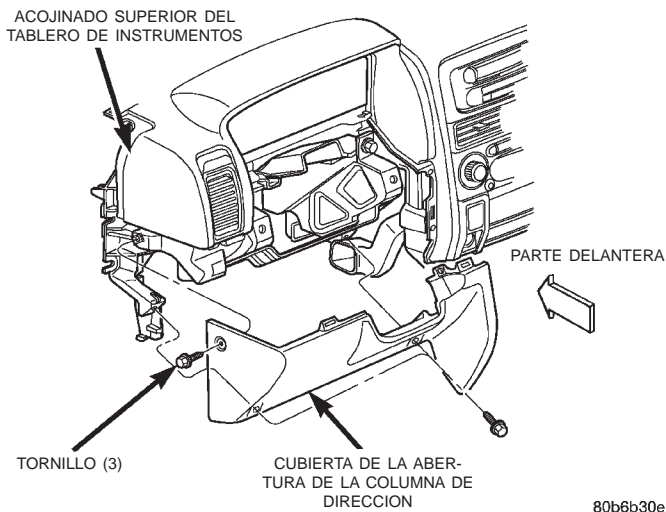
Desmontaje e instalación de la cubierta de la abertura de la columna de dirección
